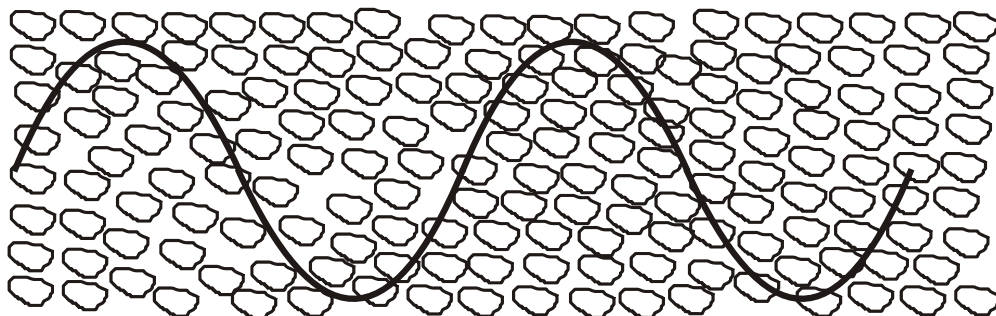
Путь режущего зерна через обрабатываемые зерна.
